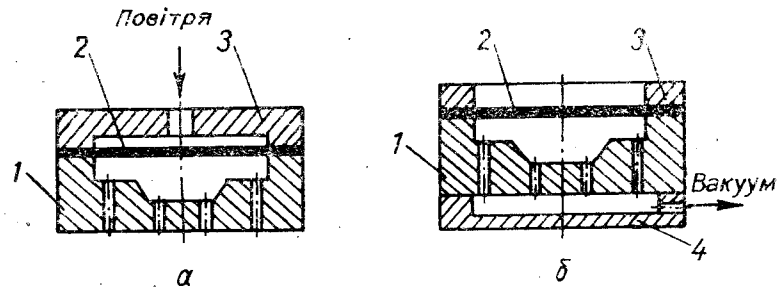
Схема пневматичного (а) та вакуумного (б) формування заготовок з листових пластмас:
